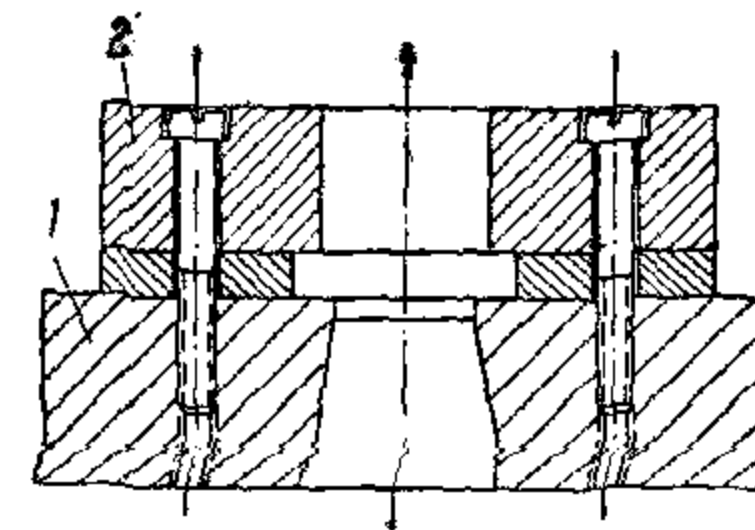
Матрица 1 вырубного штампа с направляющей плитой 2
